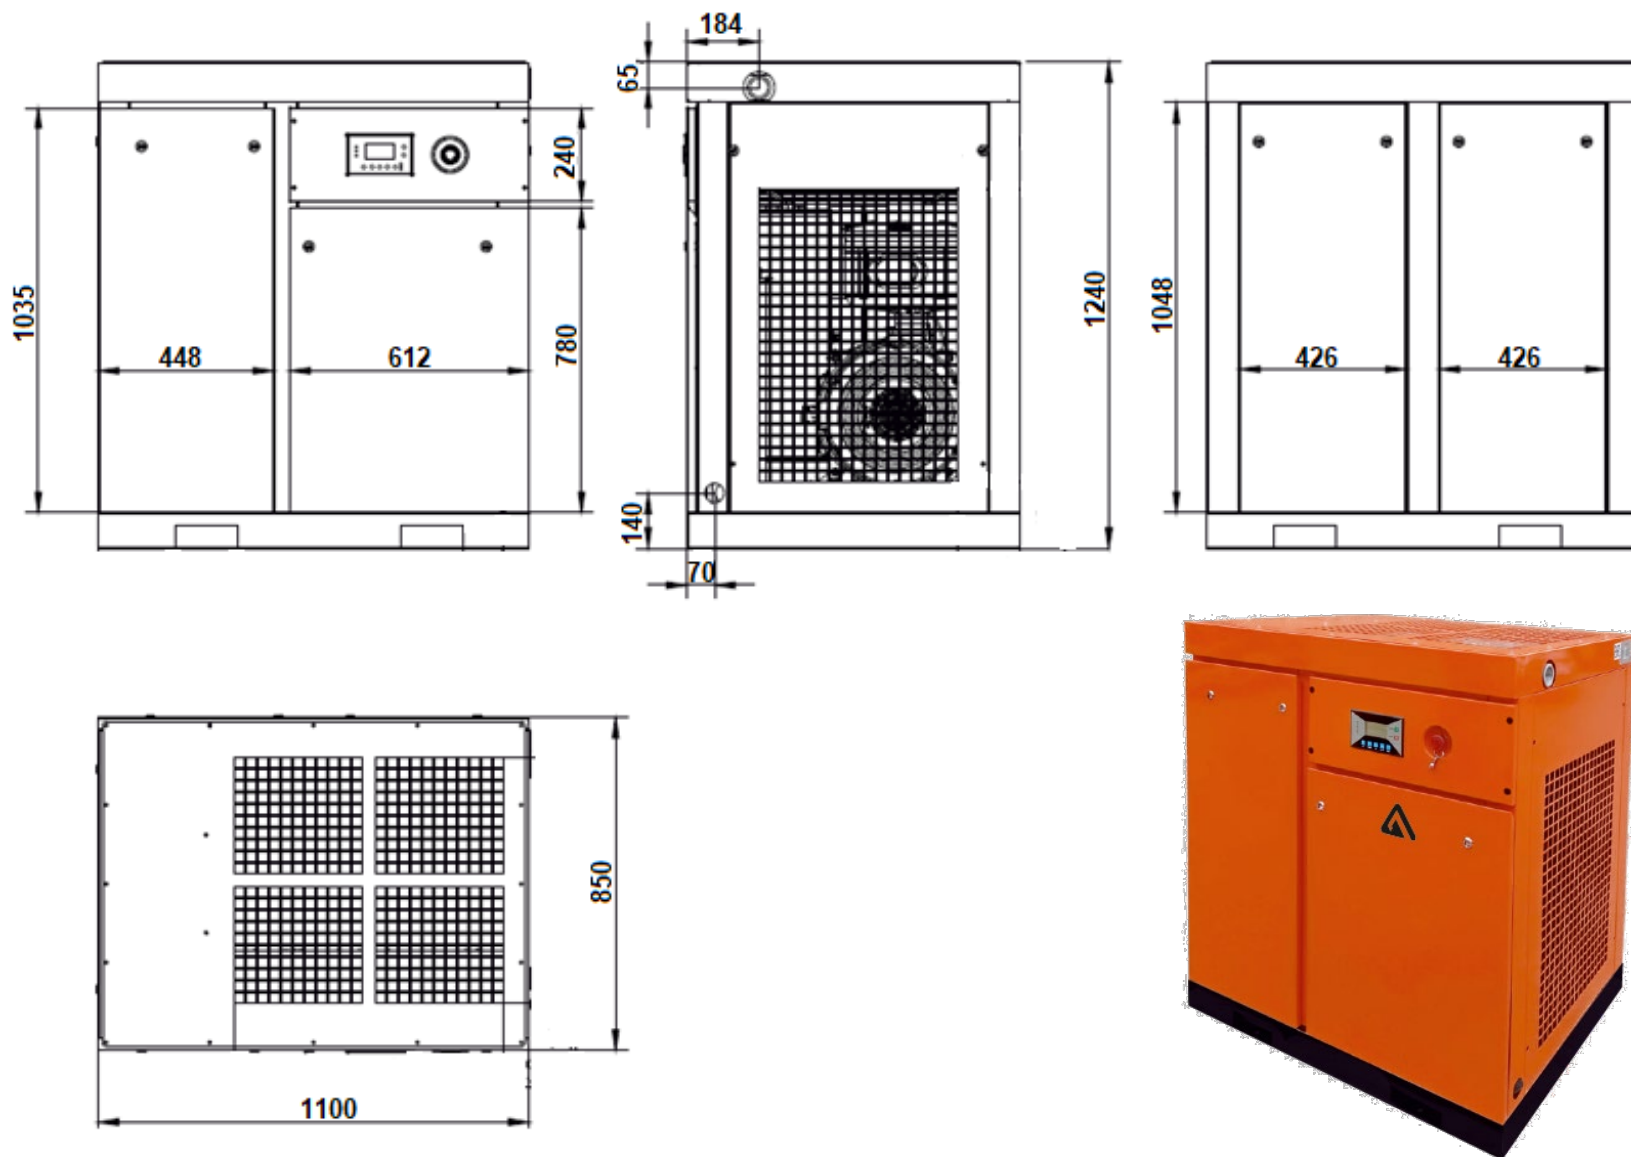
Общий вид, габаритные размеры станции компрессорной ЗИФ-СВЭ типа АРМ с двигателем 37 кВт
